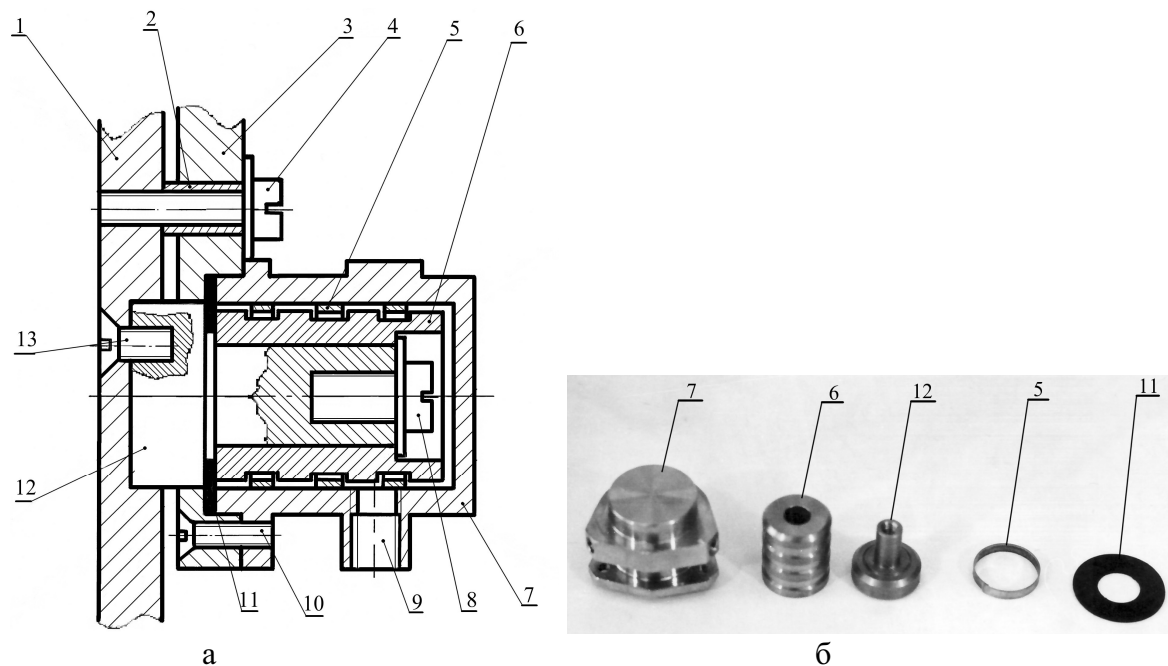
Демпфирующее устройство: а) чертёж общего вида; б) основные детали
